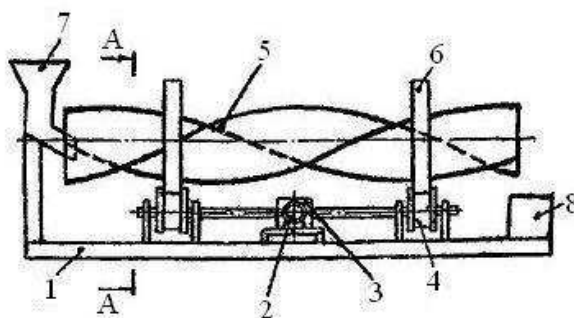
Установка для смешивания компонентов кормов, вид спереди
